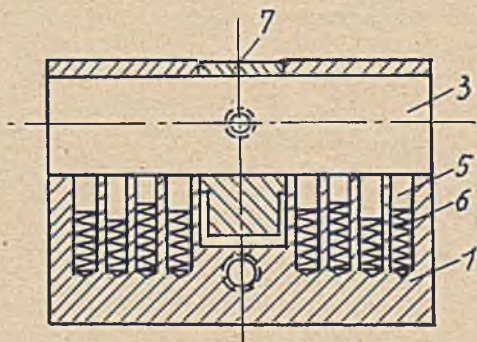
Einbau-Doppelzylinder mit durchgehendem Zylinder
